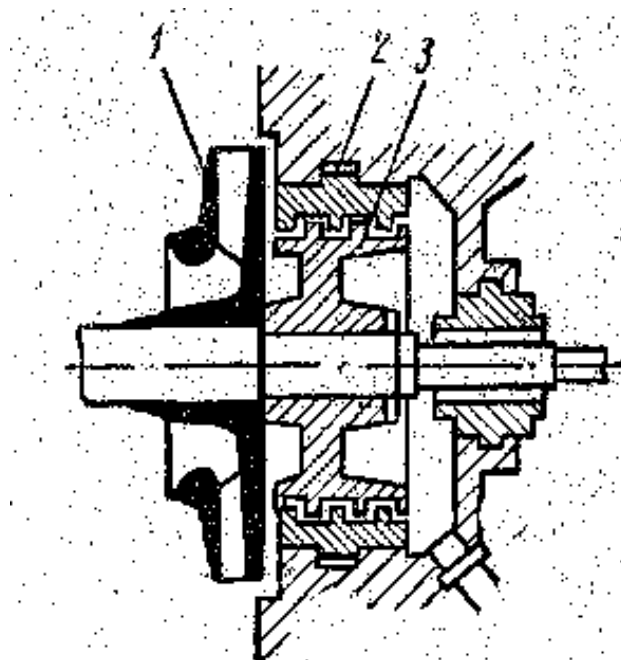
Разгрузочный поршень центробежной компрессорной машины:
